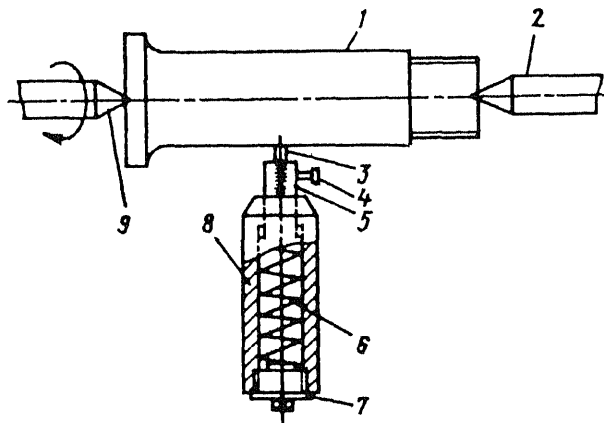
Приспособление для ФАБО валов, болтов и др. деталей:
